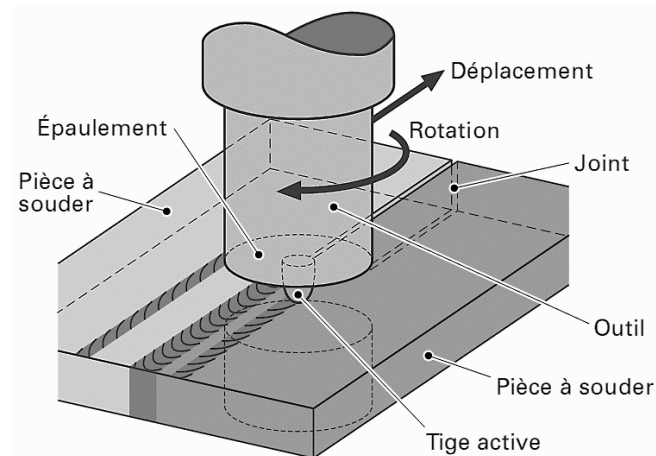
Schéma du soudage par friction malaxage [4].
